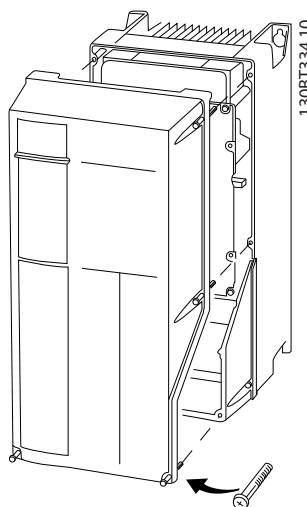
Acceso al cableado de las protecciones IP55 e IP66
